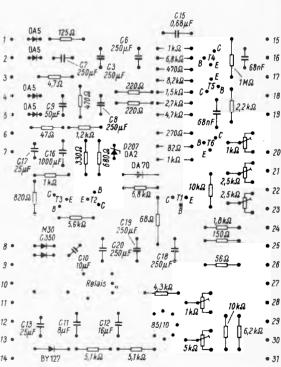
Lageplan der Bauelemente auf der nach Bild 11 hergestellten Platine (Maßstab 1 : 2)
